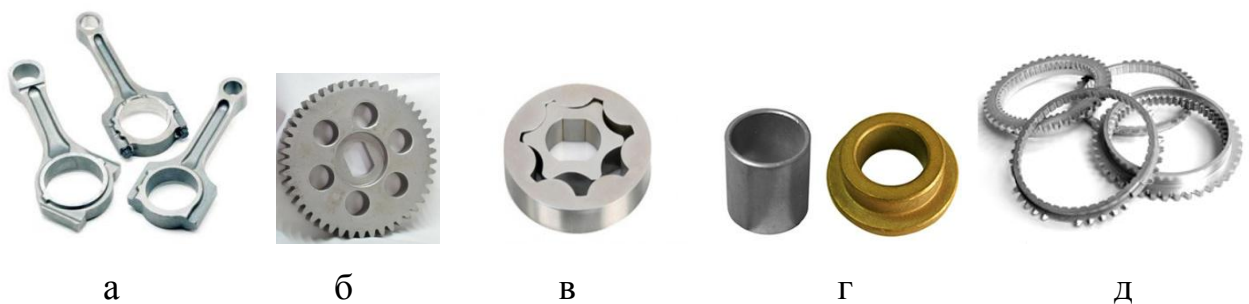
Конструкційні деталі: а - шатуни; б - шестерні; в - деталі масляного насоса; г - втулки; д - кільця блокувальні синхронізатора трактора
